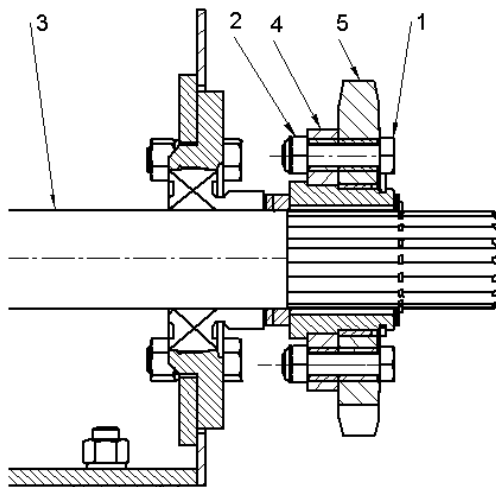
Zabezpieczenie walca dolnego(lewa strona prasy)
